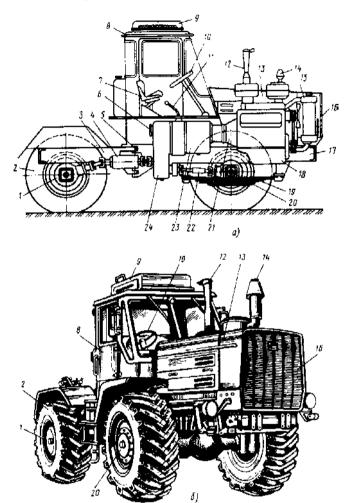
Колесный трактор Т-150К: а – компоновка основных сборочных единиц; б – общий вид; 1, 20 – грузовой и подмоторный ведущие мосты; 2 – колесо; 3, 17 – грузовая и подмоторная полурамы; 4, 5 – шарниры; 6 – фланец; 7 – сиденье; 8 – кабина; 9 – воздухоохладитель; 10 – рулевое управление; 11 – рычаг управления; 12 – выхлопная труба; 13 – капот; 14 – воздухозаборник; 15 – радиатор; 16 – решетка; 18 – двигатель; 19 – рессора; 21 – муфта сцепления; 22 – карданная передача; 23 – коробка передач; 24 – раздаточная коробка
